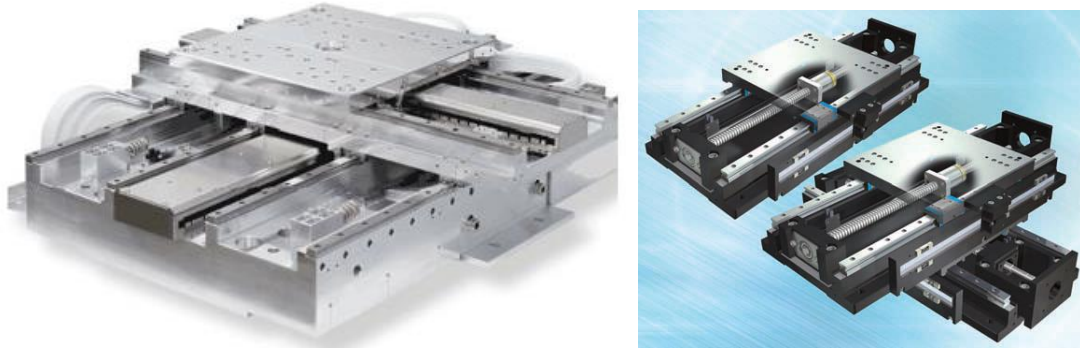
Mecanismo de posicionamiento lineal biaxial [28].
